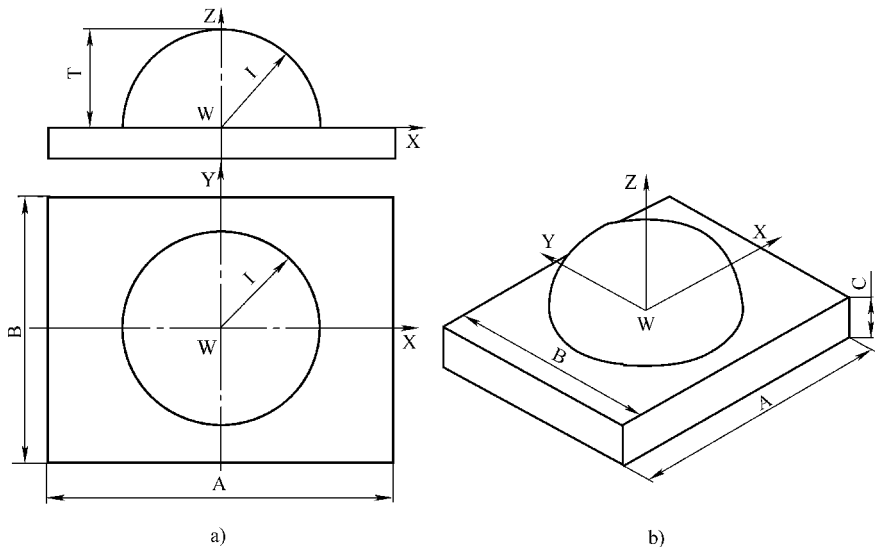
铣削加工凸半球面类零件的刀具路线示意图
